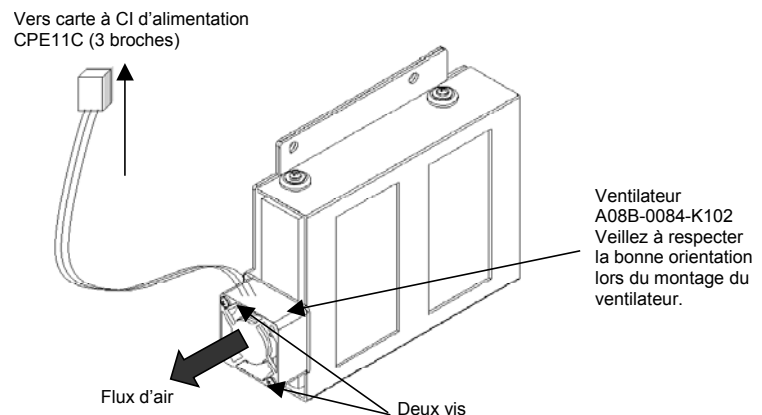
(b) Remplacement du ventilateur du lecteur de disque dur
